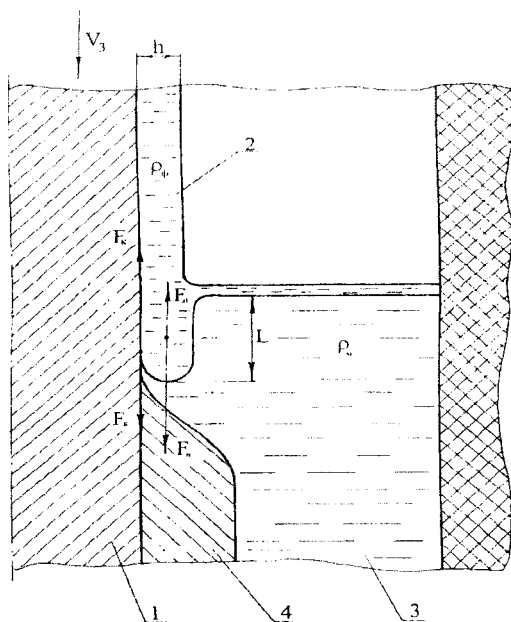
Схема к расчету скорости вытеснения флюса с вертикальной поверхности заготовки при ее погружении в расплав присадочного сплава: 1 – заготовка; 2 – слой расплава флюса; 3 – расплав присадочного сплава; 4 – слой наможенного сплава
